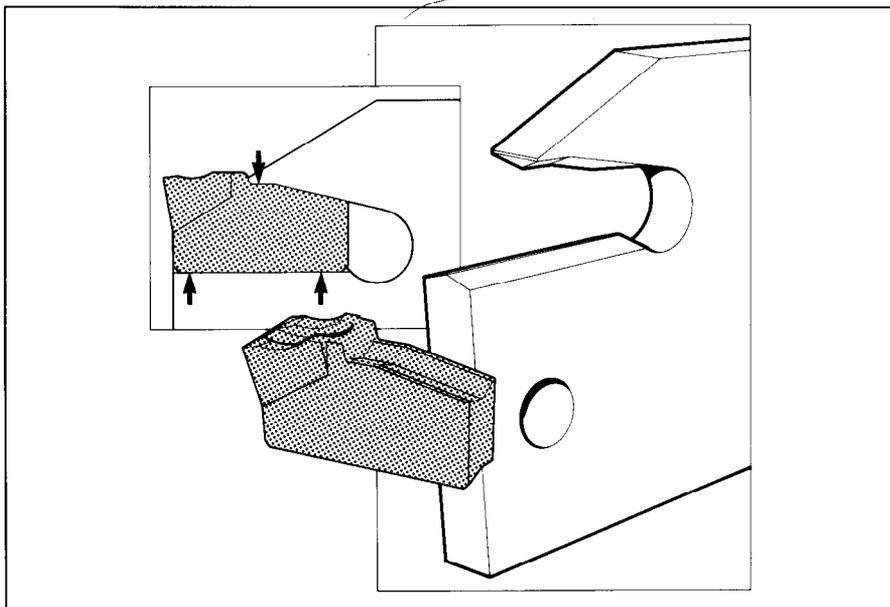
Stechwerkzeug in Wendeschneidplattenausführung
